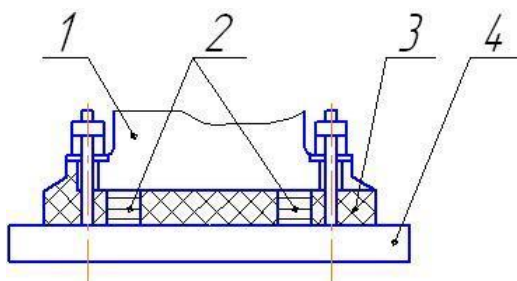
Схема установки устаткування на фундамент, на пакети підкладок:
